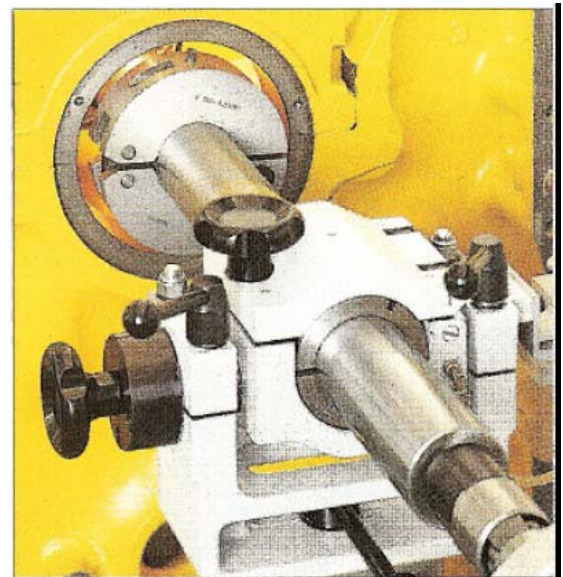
Расточка коренного подшипника резцом, закрепленным в браслетном резцедержателе.
